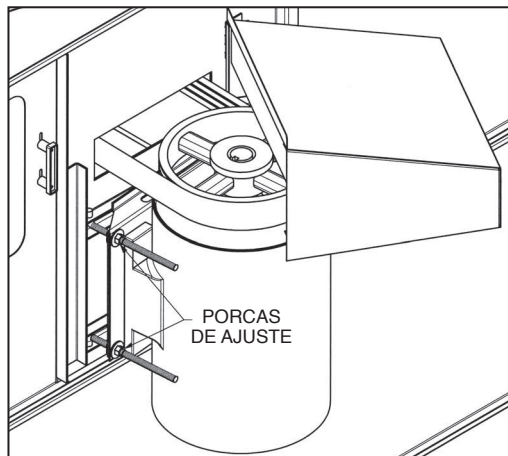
Motor Montado Externamente, Tiragem Induzida
